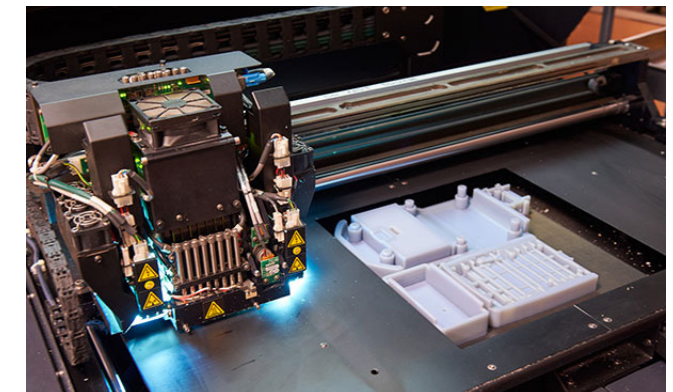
Cabezal de impresión (izquierda) y partes fabricadas (derecha) en una máquina polyjet.
